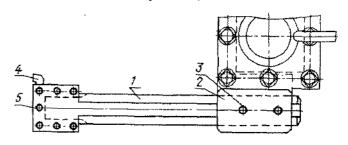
Резцовая оправка для обработки деталей над выемкой в станине
